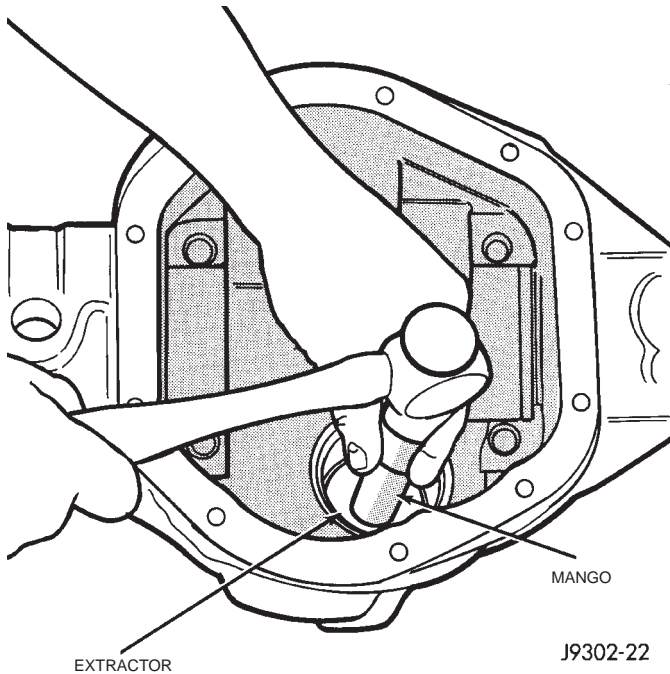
Desmontaje de la cubeta del cojinete delantero
